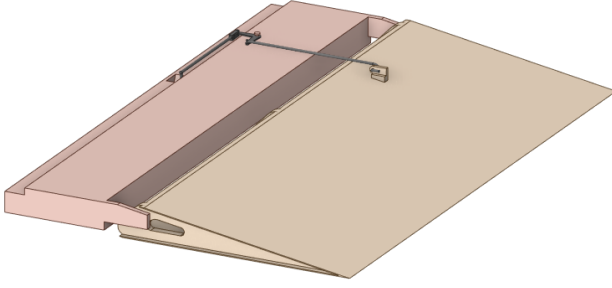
Eğitim seti için yapılan iniş takımı CAD tasarımı
